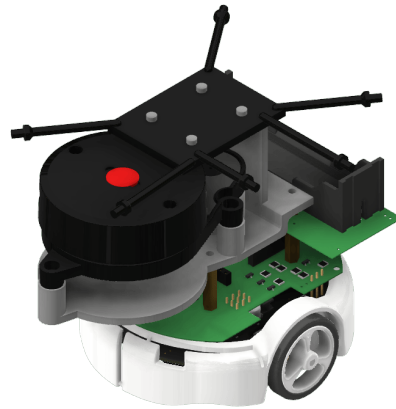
Vista isométrica del montaje frontal del sensor FHL-LD20 en Pololu 3pi+
